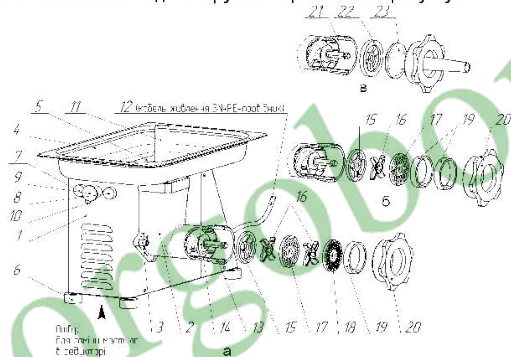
Загальний вигляд м'ясорубки: 1 - привод; 2 - корпус м'ясорубки; 3 - втулка зажимна; 4 - чаша; 5 - захисний бар'єр; 6 - опора; 7 - кнопка "ПУСК"; 8 - кнопка "РЕВЕРС"; 9 - кнопка "СТОП"; 10 - лампа сигнальна "Мережа"; 11 - товкач; 12 - кабель живлення (3N+PE - провідник; 13 - шпонка; 14 - шнек; 15 - ніж підрізний; 16 - ніж двосторонній; 17 - решітка з отворами 9 мм; 18 - решітка з отворами 5 мм; 19 - кільце ущільнюоче; 20 - гайка зажимна; 21 - стопорне кільце; 22 - підтримувач; 23 - насаддя.
